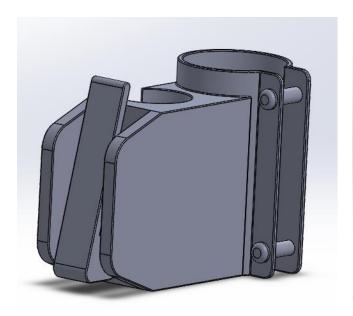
Vista pieza 1 mecanismo estructura-respaldo.
